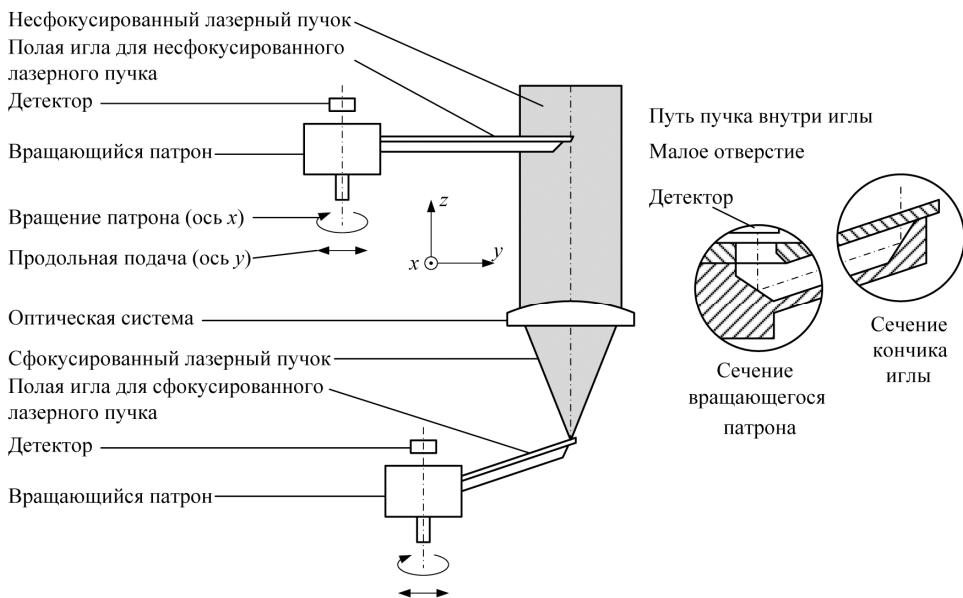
Схема прибора PROMETEC LASERSCOPE UFF 100
